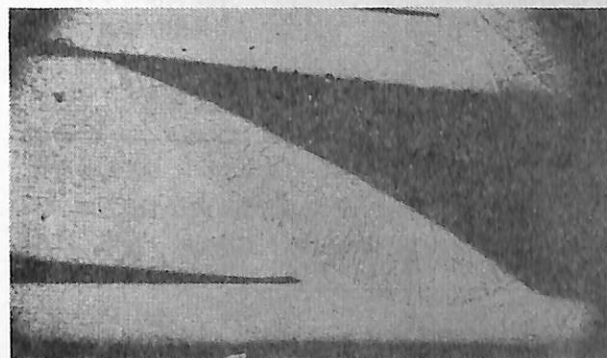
Fillet weld between 1.5 mm and 0.5 mm Invar sheets. (文献 iii)
